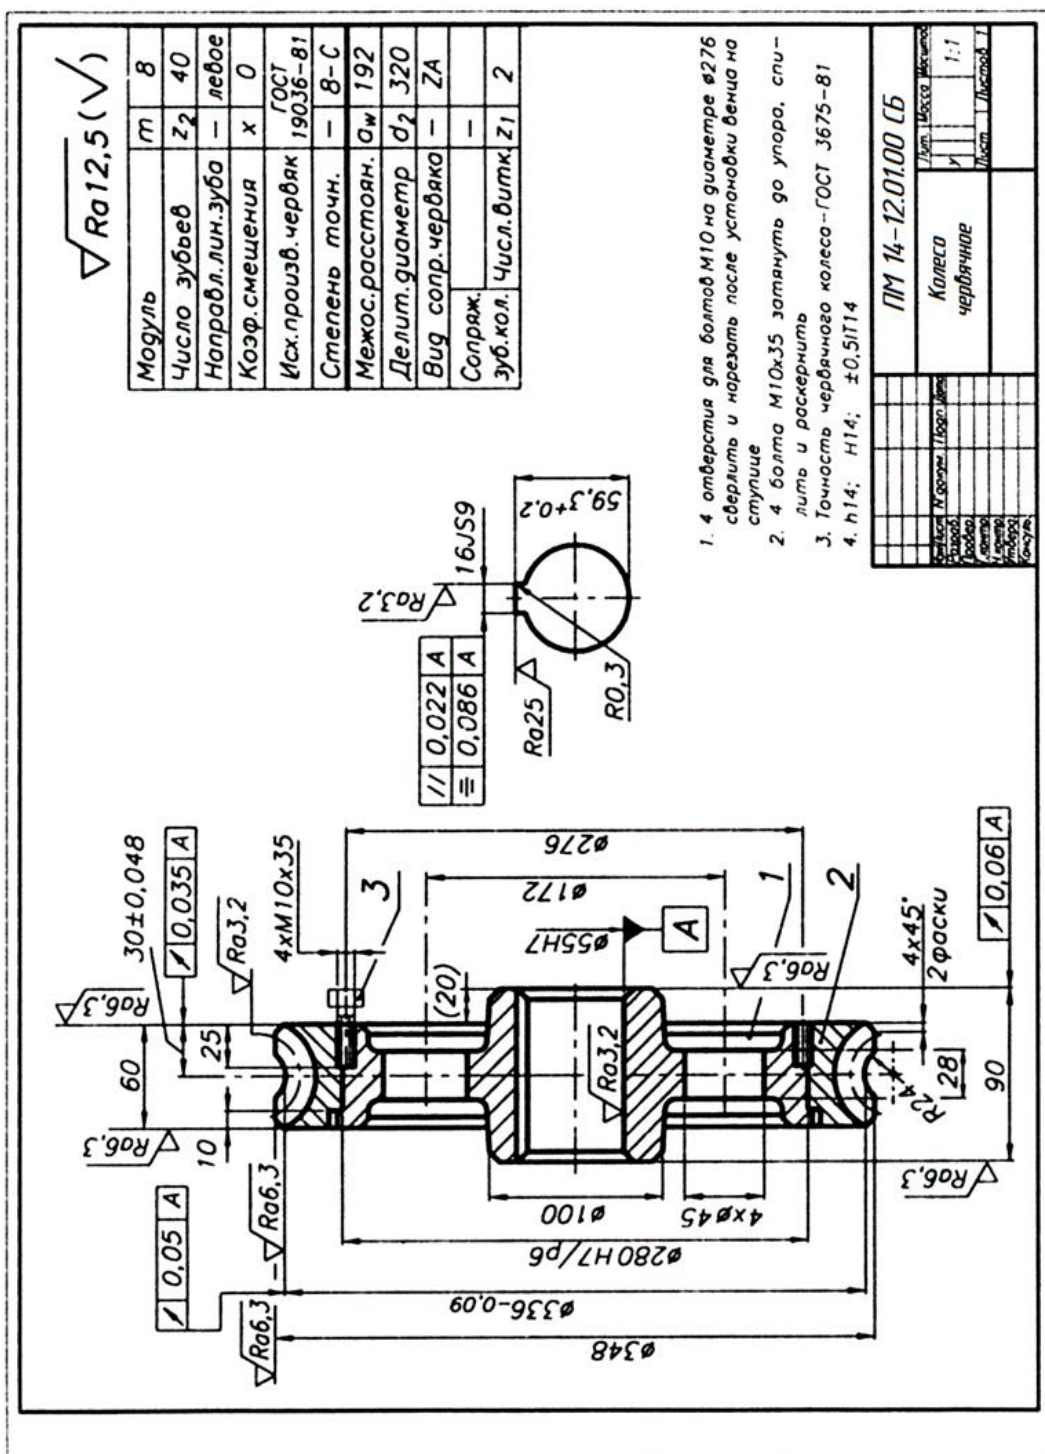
Пример рабочего (сборочного) чертежа червячного колеса
